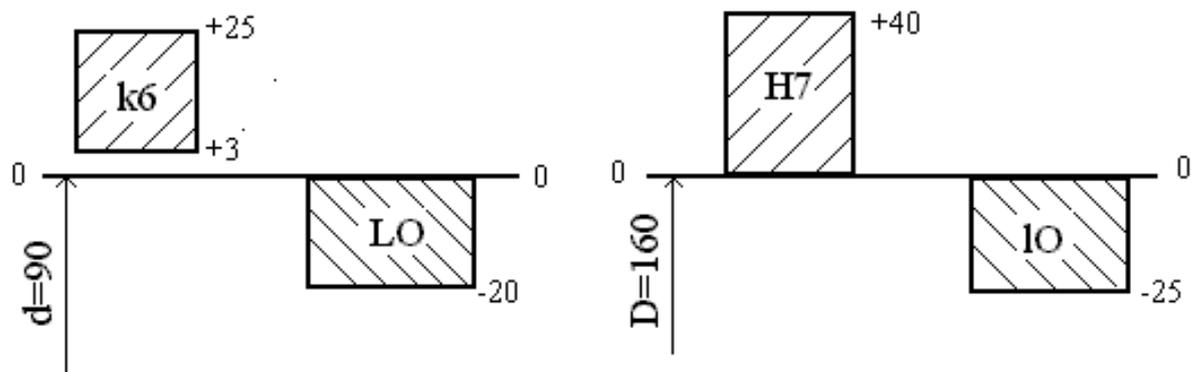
Схема расположения полей допусков колец подшипника и сопрягаемых с ними деталей
